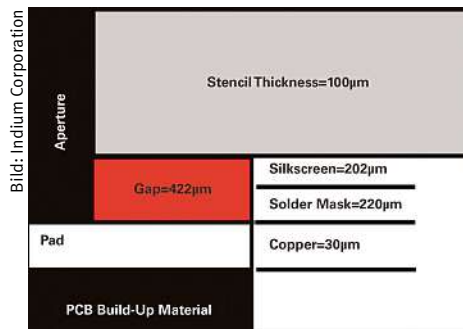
PCB-Siebdruck auf der Oberseite von Lötstopmmaske und Kupfer.
